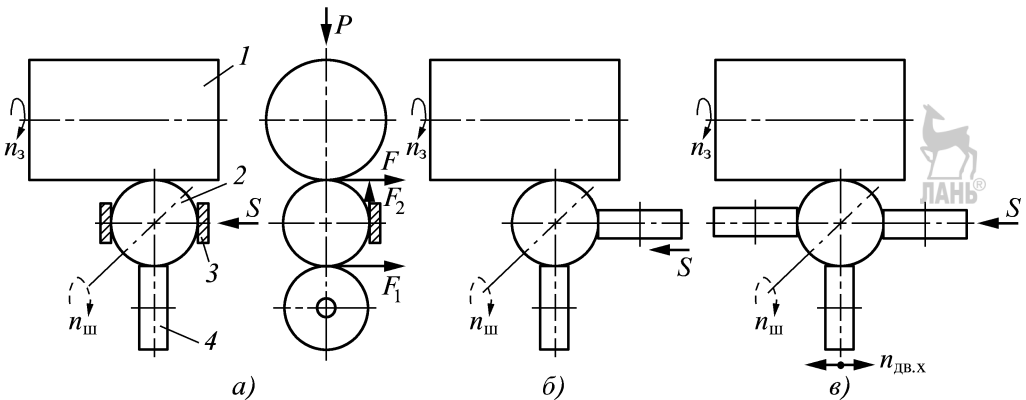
Схема конструкций одношариковых обкатников с опорой шариков на шарикоподшипники:
